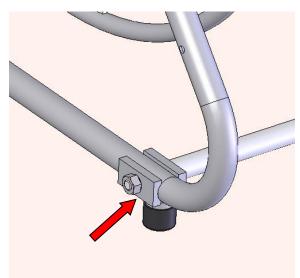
Bodenauflage 3-teilig verschweisst mit angeschraubter Verbindungsstange.
